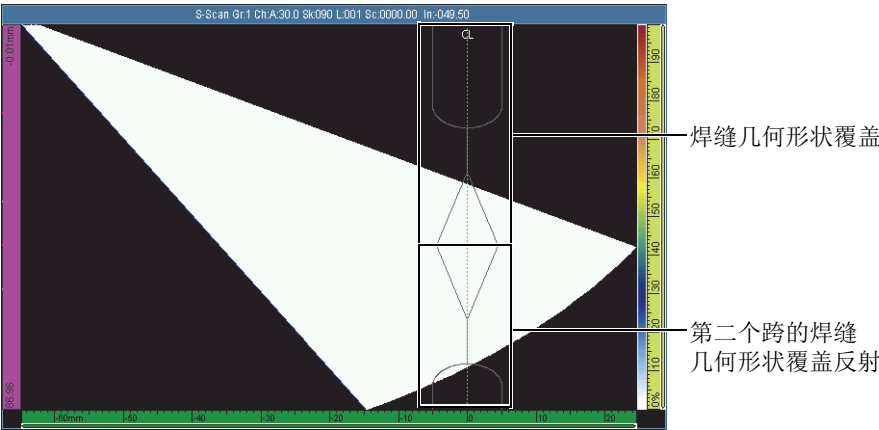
J 形焊缝几何形状覆盖的示例
